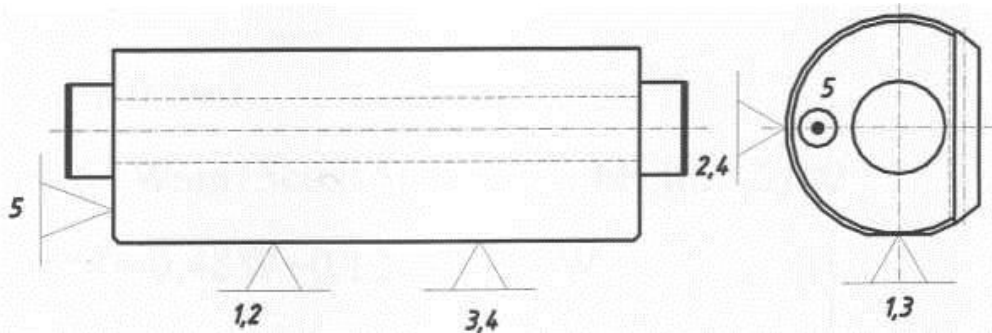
Схема установки заготовки Рейка зубчата ПЭА 01.40.01.603А
